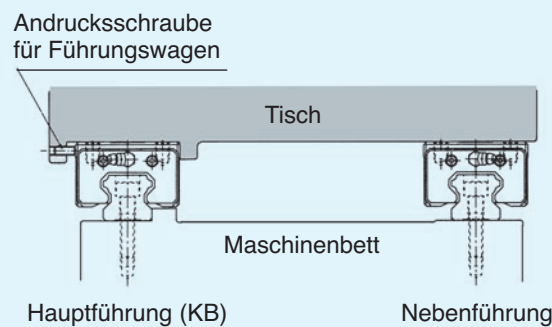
Beispiel für Montage ohne Andruckschrauben für Führungsschienen auf der Hauptführungsseite
